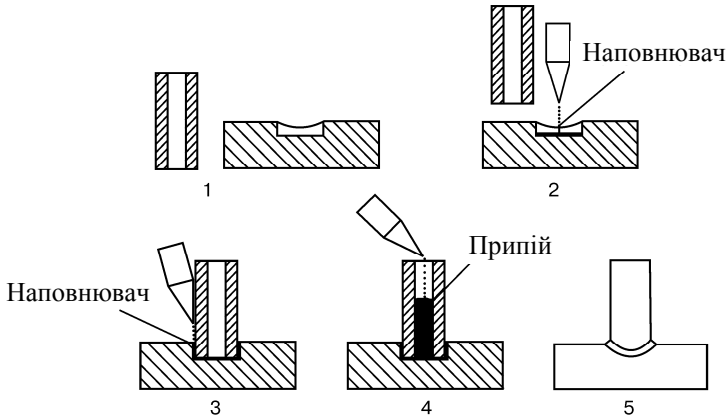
Схема збирання деталей для паяння при широкому зазорі з наповнювачем: 1 – деталі перед збиранням; 2 – заповнення стикової частини шва наповнювачем; 3 – заповнення телескопічної частини шва наповнювачем; 4 – заповнення технологічної порожнини припоєм; 5 – вузол після паяння
